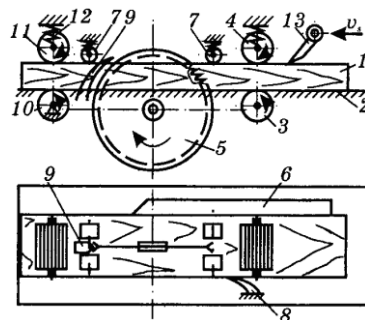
Принципова схема круглопилкового верстата: 1 – заготовки; 2 – стіл; 3, 4 – передні подавальні вальці; 5 – кругла пилка; 6 – напрямна лінійка; 7 – ролики; 8 – боковий пружинний притискач; 9 – розклинювальний ніж; 10, 11 – задні подавальні вальці; 12 – пружини; 13 – кігті
